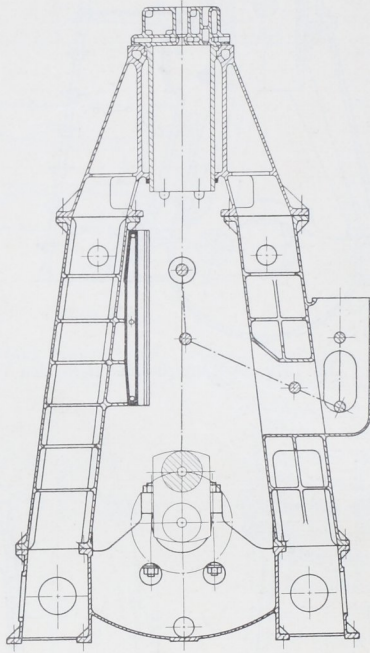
Rahmen einer stehenden Schiffsdieselmachine. Ständer in der Kröpfungebene.
